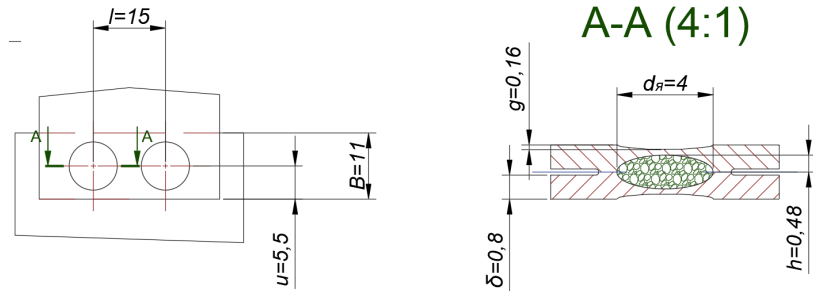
Розміри конструктивних елементів зварного з'єднання деталей 0,8 мм
